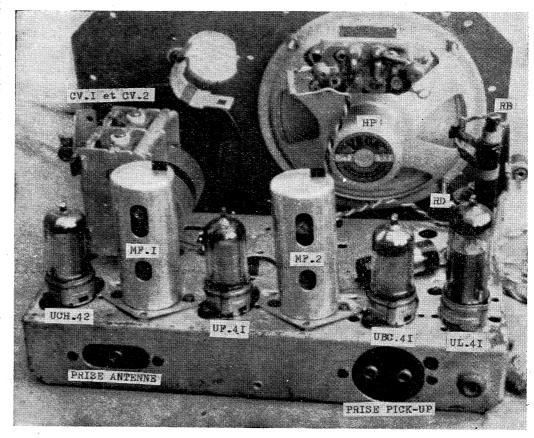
Disposition des pièces sur le dessus du châssis.
